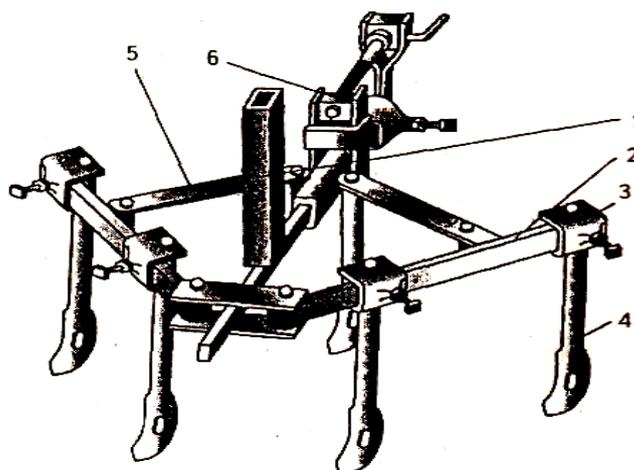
Культиватор кр-70: 1 – стойка; 2 – каркас; 3 – держатель; 4 – лапа; 5 – планка; 6 – механизм регулировки
